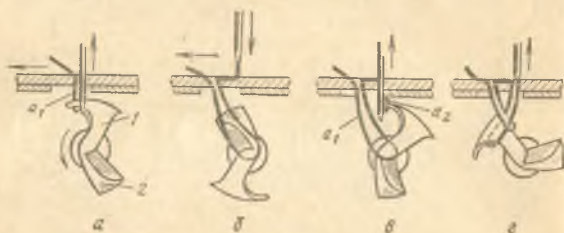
Процесс образования стежка односторонней стачивающей строчки
